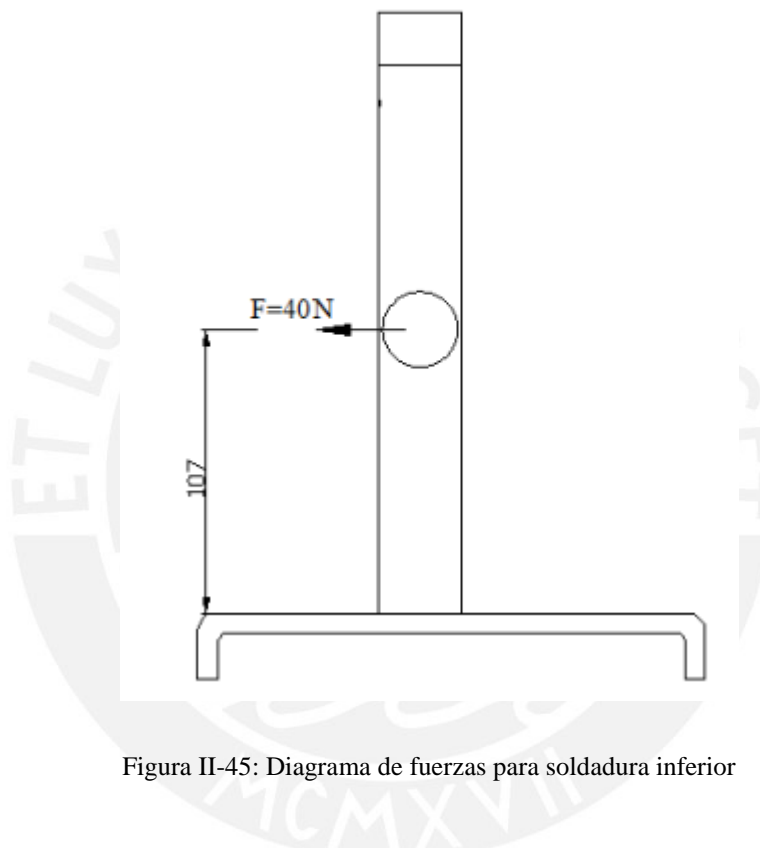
Diagrama de fuerzas para soldadura inferior
